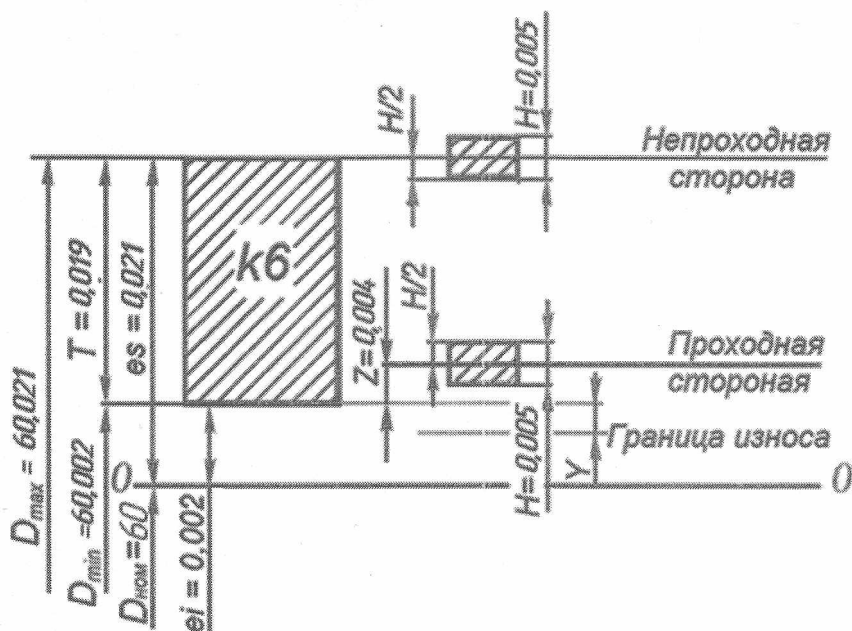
Схема рабочего эскиза калибра-скобы 60k6
